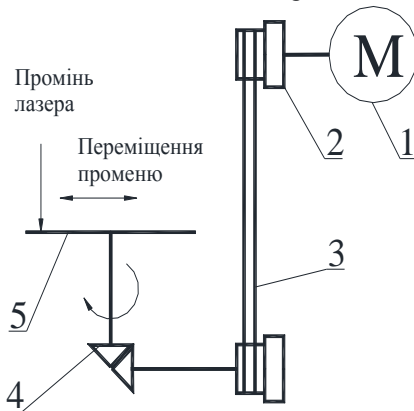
Принципова кінематична схема для лазерної обробки дискових робочих органів:
